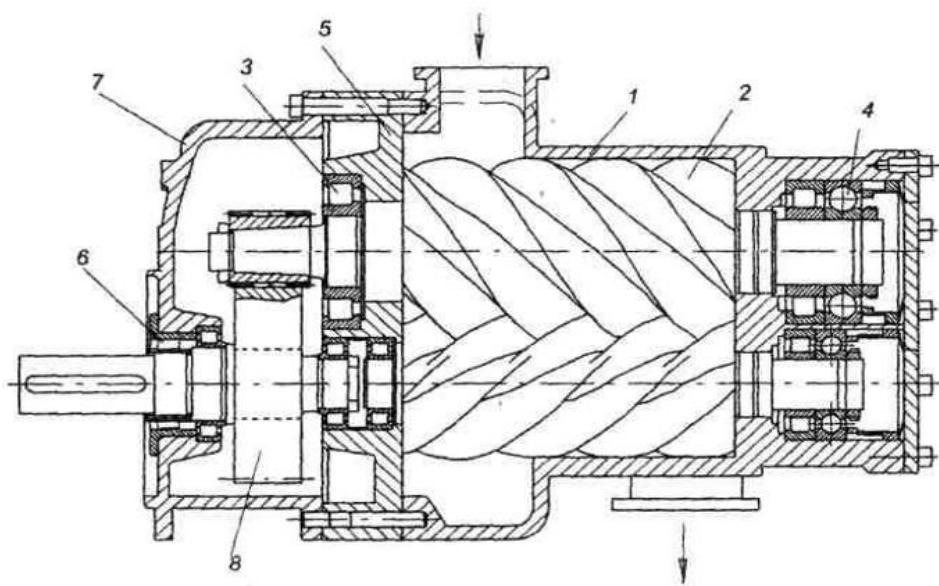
Гвинтовий компресор CF246G: 1 – корпус роторної пари; 2 – роторна пара; 3 – роликопідшипник;
